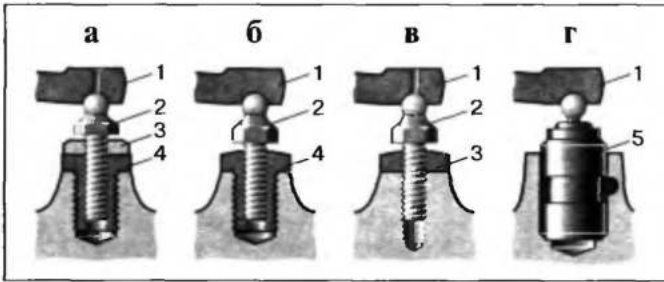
Опоры рычага привода клапана: а — с контргайкой; б — с "тугой" резьбой; в — без втулки для чугунных головок двигателей; г — с гидрокомпенсатором зазора; 1 — рычаг; 2 — опора; 3 — контргайка; 4 — втулка; 5 — гидрокомпенсатор
